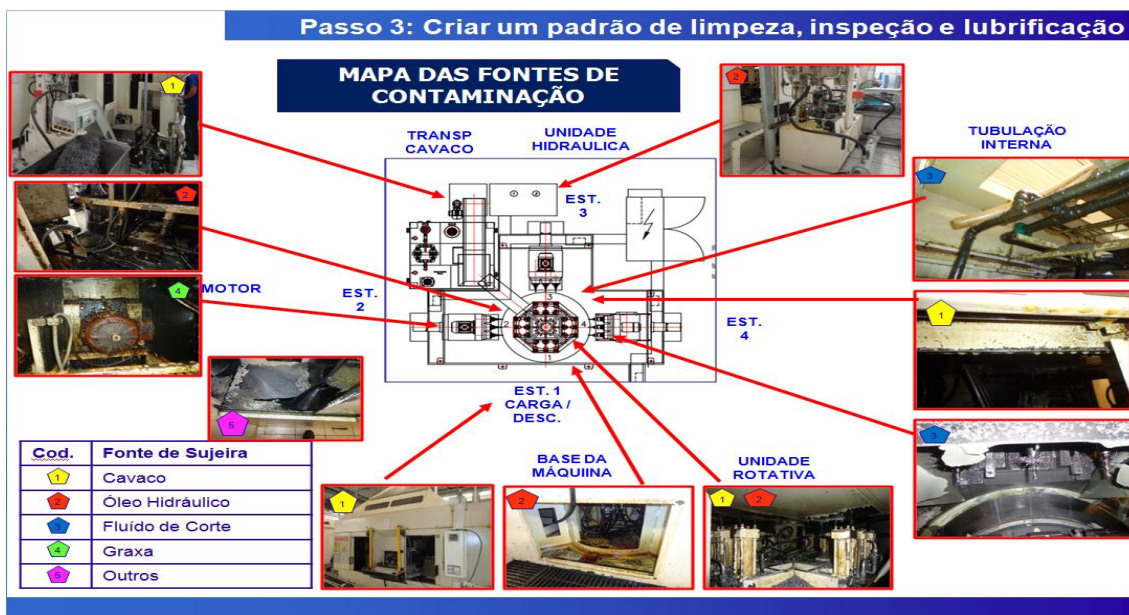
Desenho da máquina detalhando cada ponto de inspeção de limpeza e lubrificação
